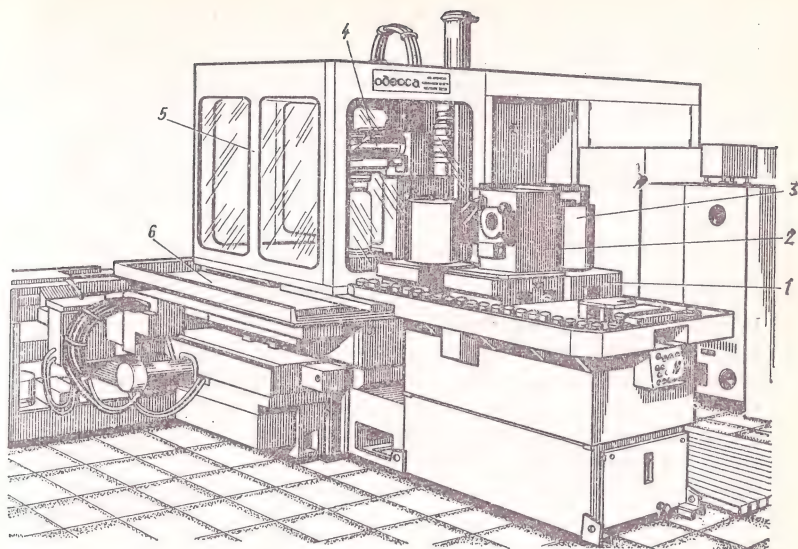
Гибкий производственный модуль обработки корпусных деталей
